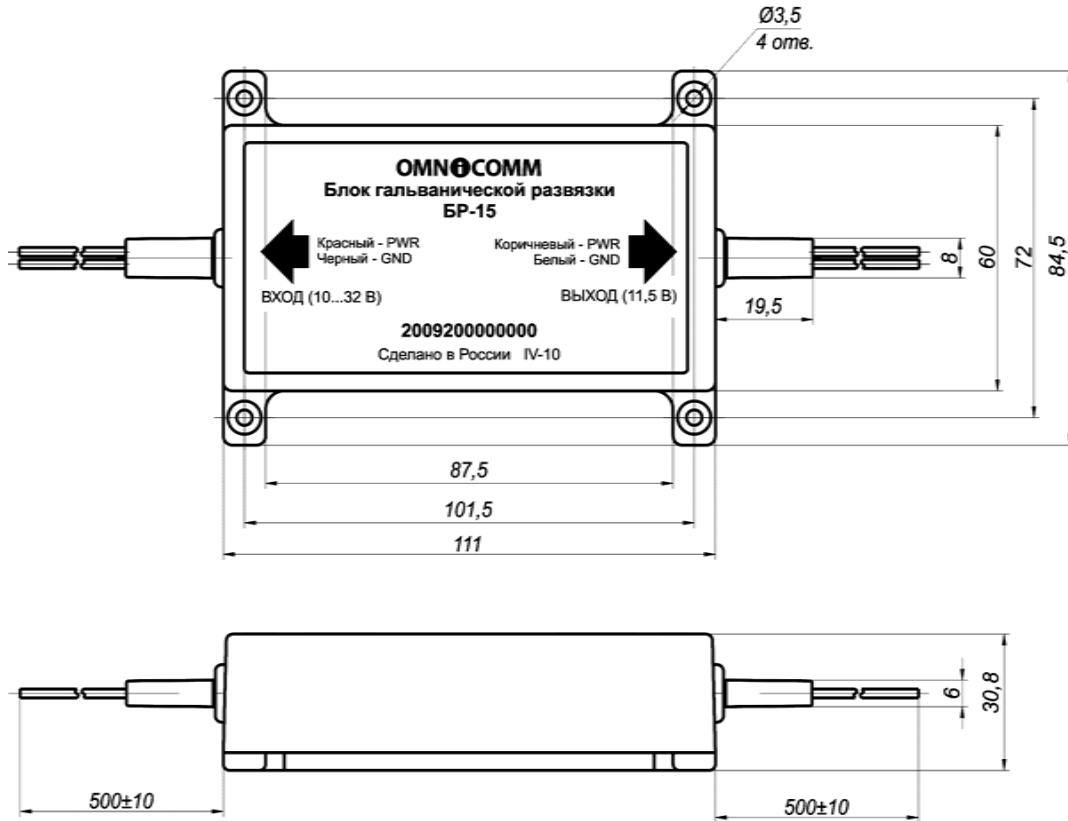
Габаритный чертеж Блока гальванической развязки БР15
